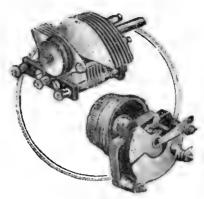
Специальный коротковолновый конденса-J B (вверху) и уравнительный воздушный конденсатор Colvern
